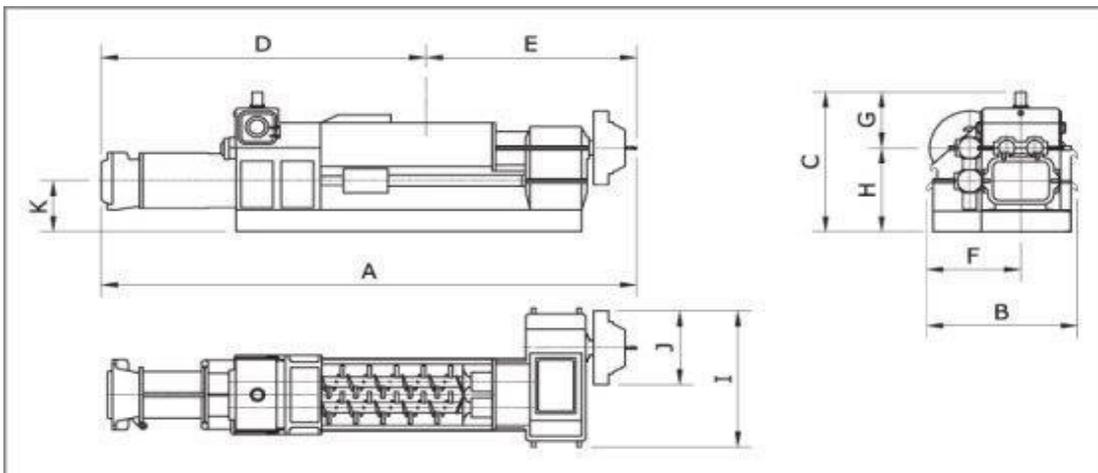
Vista de Dimensiones de extrusora MVMB500
